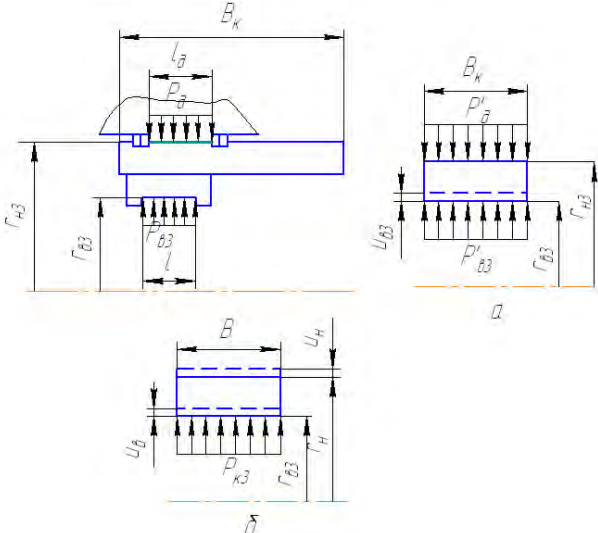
Вид опоры с наружным кольцом подшипника и расчетные схемы: а – при натяге; б – при зазоре
